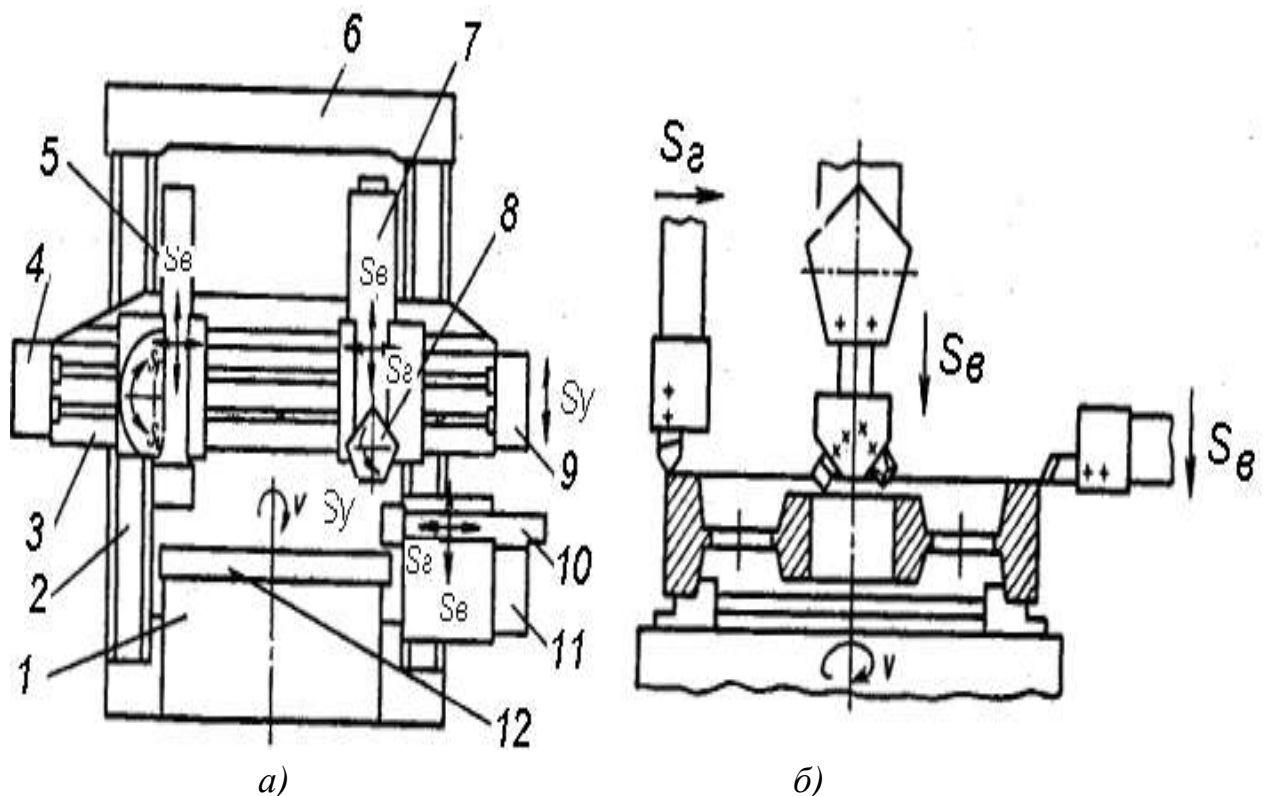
Схеми токарно-карусельного верстата (а) і обробки на ньому заготовки (б)
